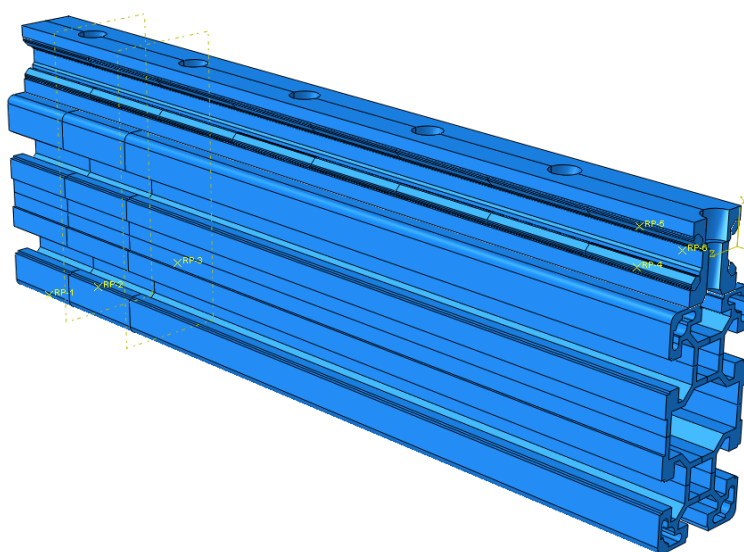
Vizualizace MKP výpočtu tlaku spoje střední příčky
